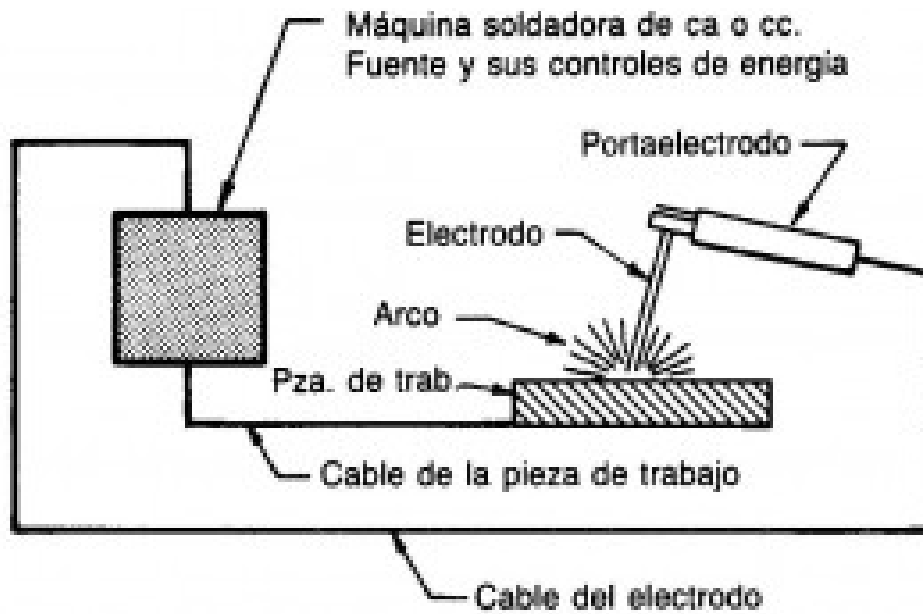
Soldadura por arco. [I-41]
